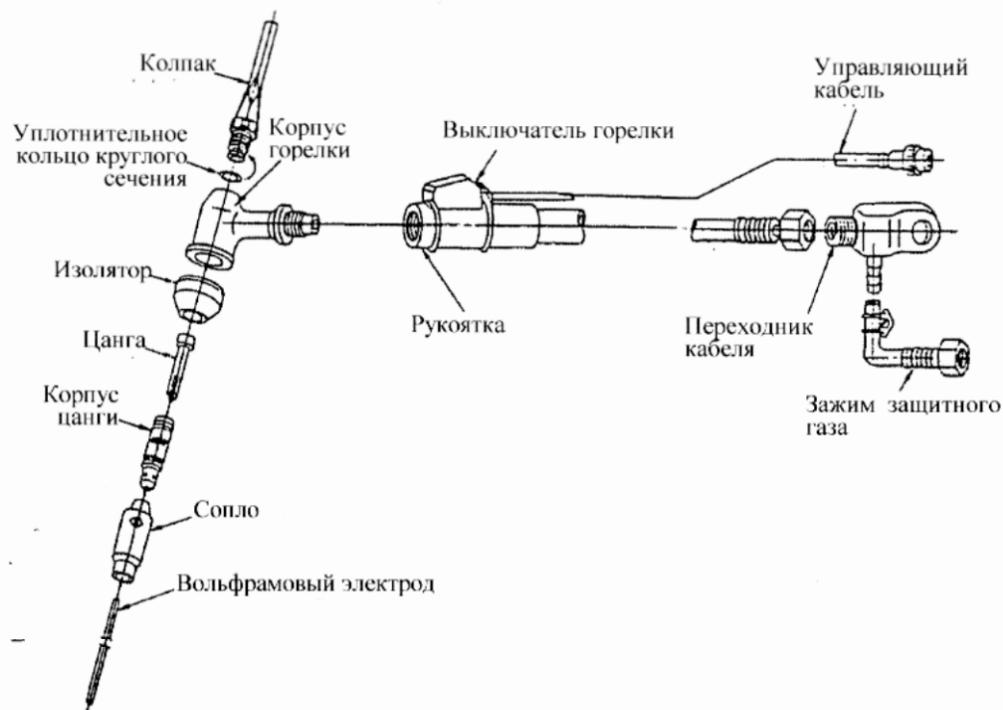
Конструкция горелки воздушного охлаждения для Аргонодуговой сварки
